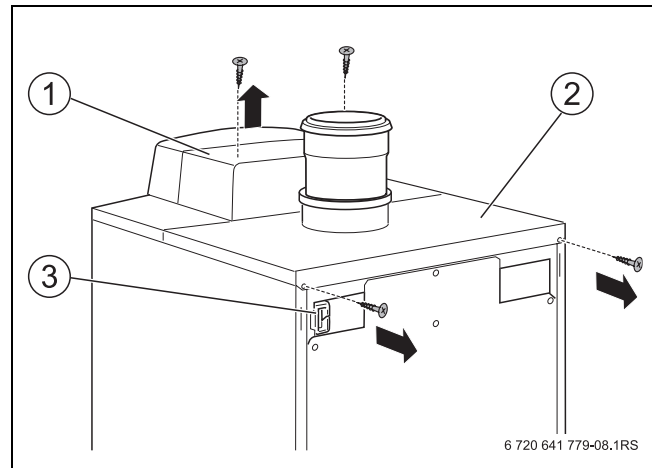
Retirer le couvercle et le capot arrière de la chaudière
